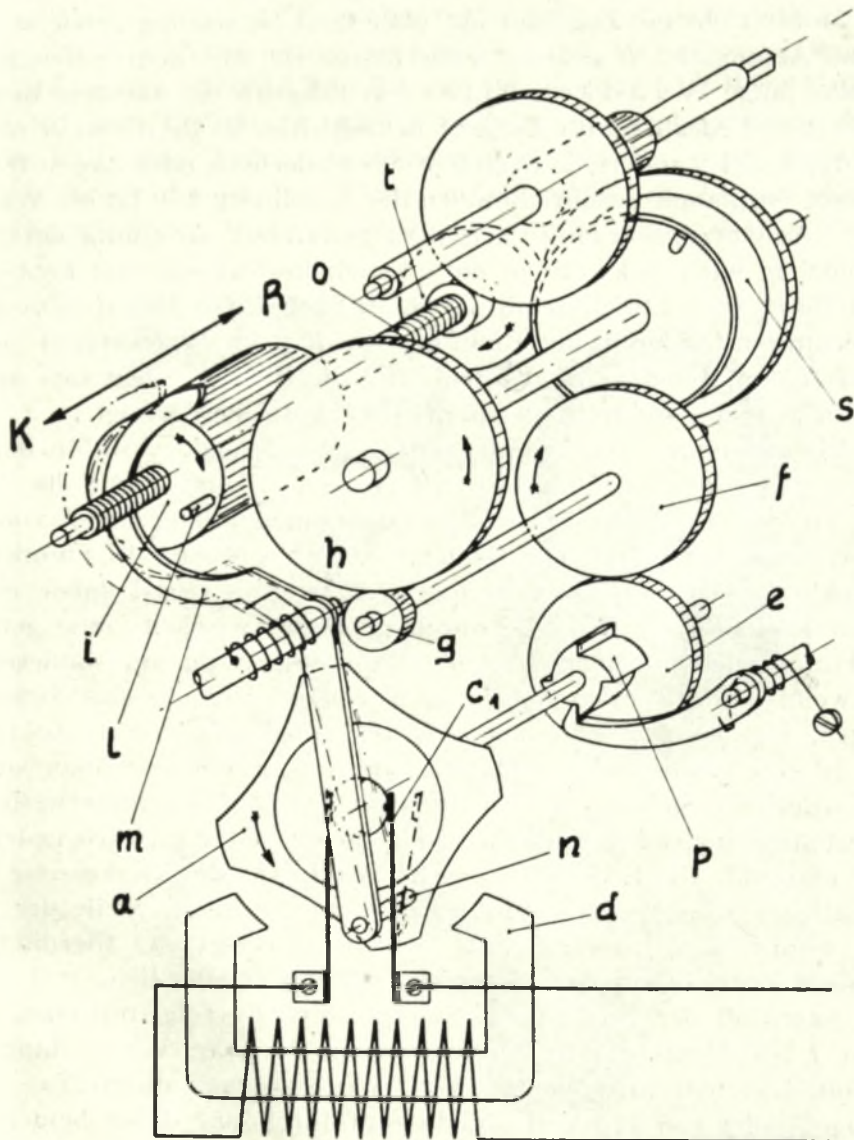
Heliowatt-Uhr mit Universal-Kollektormotor
